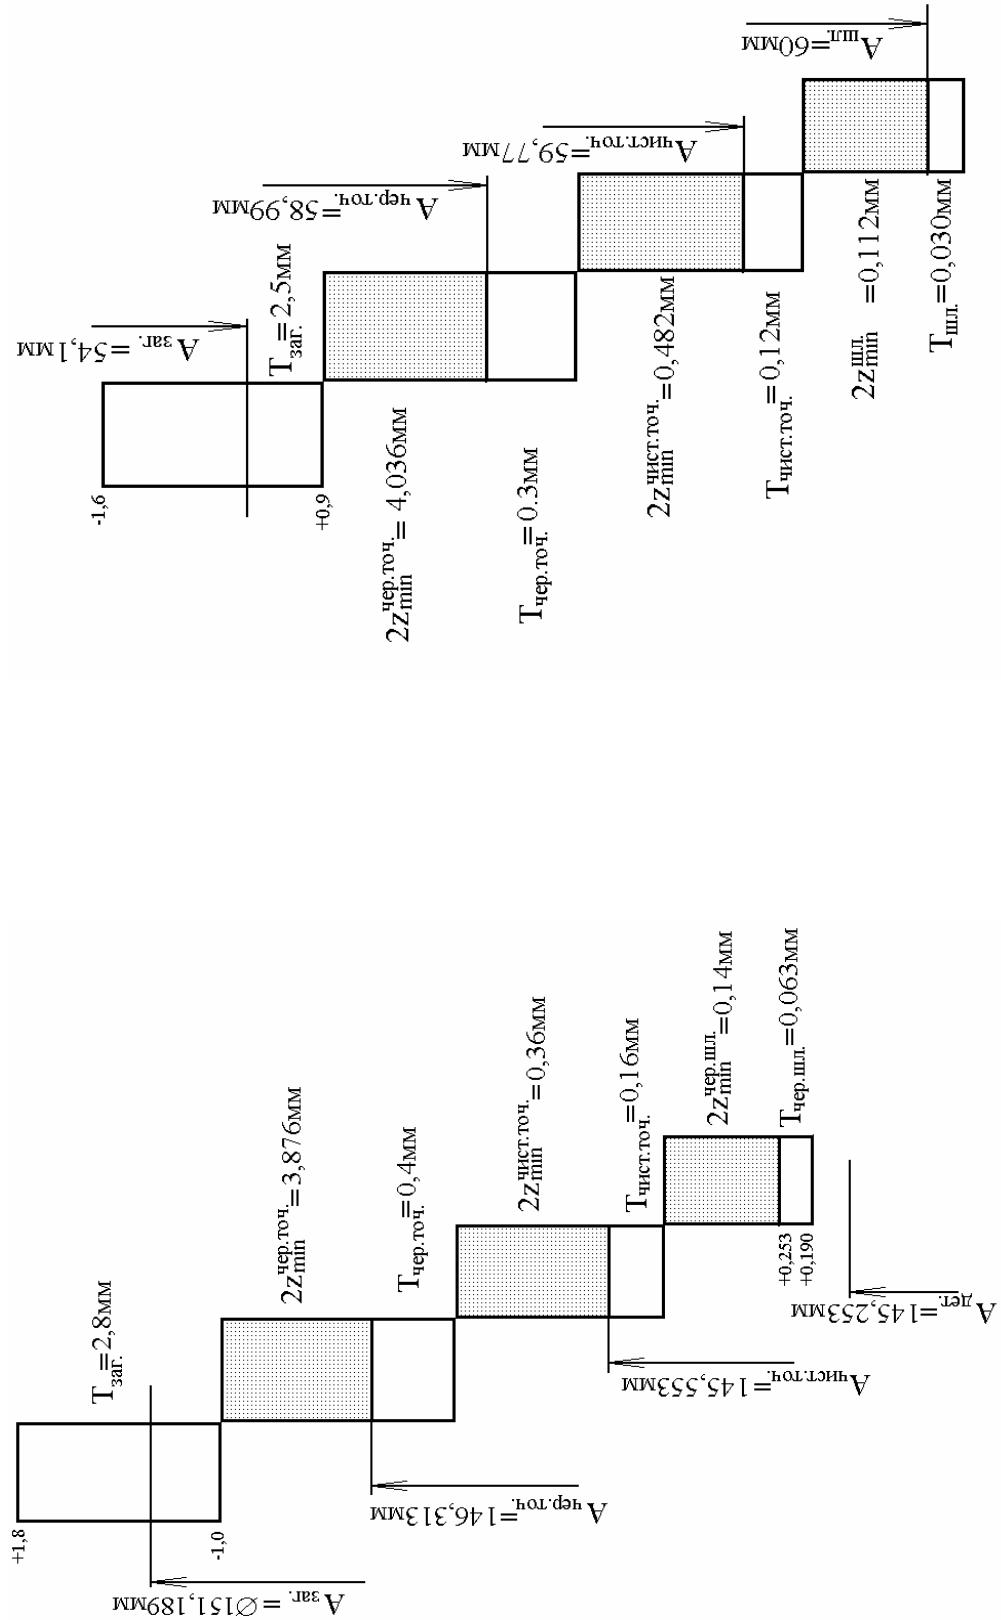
Схема расположения допусков и припусков для определения операционных размеров наружной цилиндрической поверхности $\varnothing 145\text{u}8$
